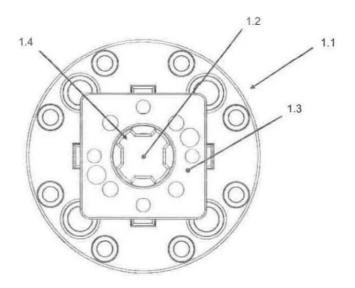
Vista en planta superior del mandril de apriete y la plataforma, con la barra tractora en posición bloqueada
